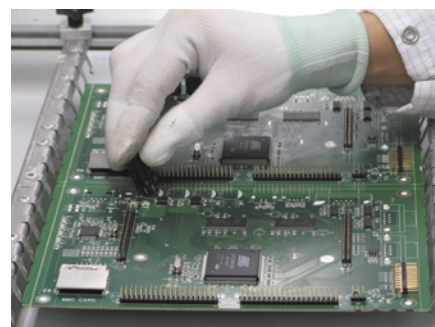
Płytki przygotowane do montażu przewlekane (THT)
